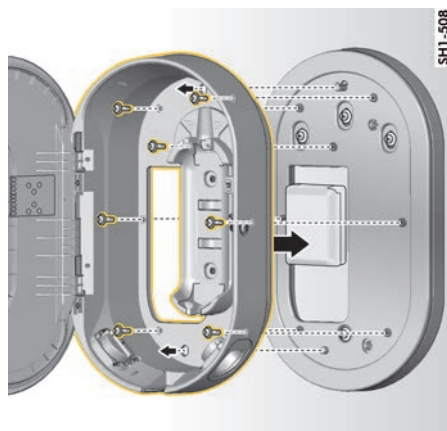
Atornillado del puerto de carga en la placa de montaje
